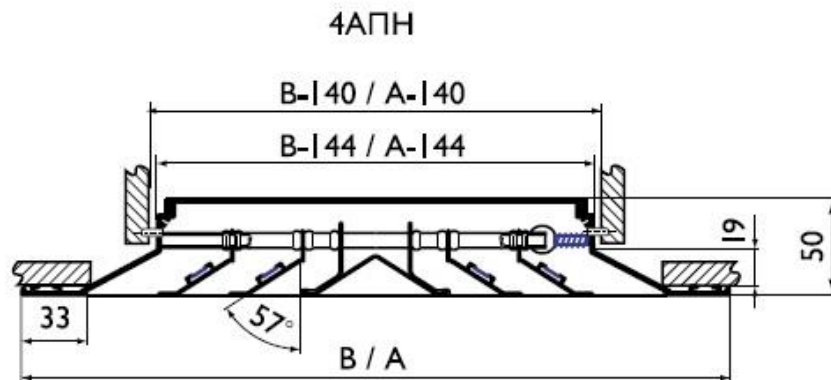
Конструктивная схема воздухораспределителя 4АПН
